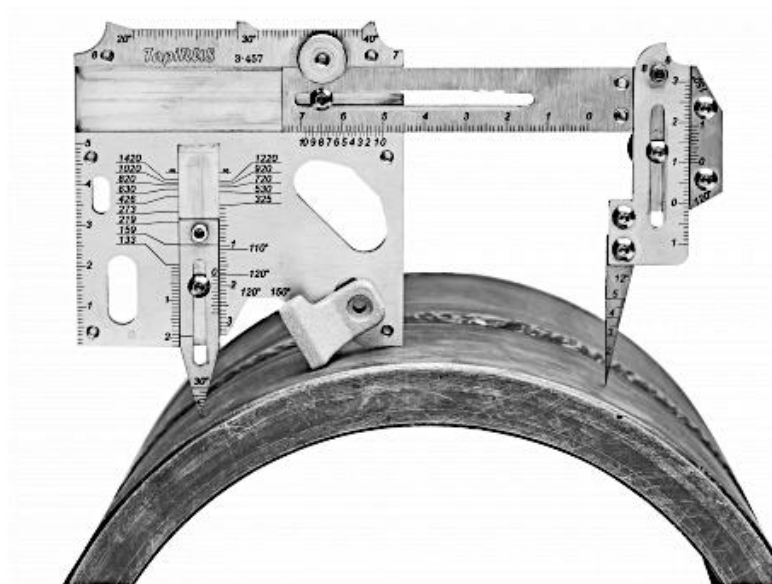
Универсальный шаблон сварщика (УШС) ТаріRUS [5]
